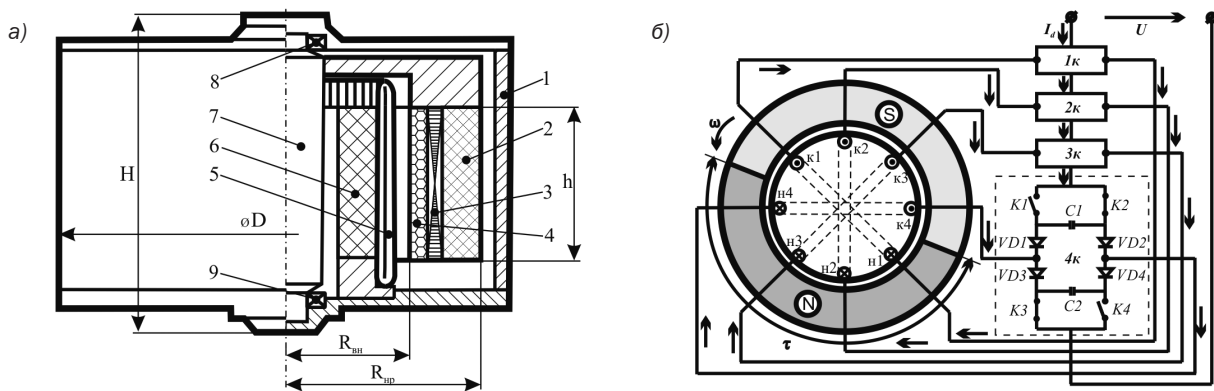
Инерционный накопитель энергии: а) устройство аккумулятора; б) схема СЭМПЭ: 1 — вакуумный кожух; 2 — маховик; 3 — ферромагнитный экран; 4 — постоянные магниты; 5 — обмотка якоря; 6 — корпус статора; 7 — вал; 8, 9 — подшипниковые узлы; H , D — габаритные высота и диаметр накопителя; $R_{вн}$, $R_{нр}$ — внутренний, наружный радиусы маховика; h — высота маховика; ω — частота вращения ротора; τ — полюсное деление; $n1$, $n2$, $n3$, $n4$ и $k1$, $k2$, $k3$, $k4$ — начала и концы секций катушек якоря соответственно; $1к-4к$ — коммутаторы; $K1$, $K2$, $K3$, $K4$ — ключи; $VD1$, $VD2$, $VD3$, $VD4$ — диоды; $C1$, $C2$ — конденсаторы; I_d — ток источника; U — напряжение на зажимах
